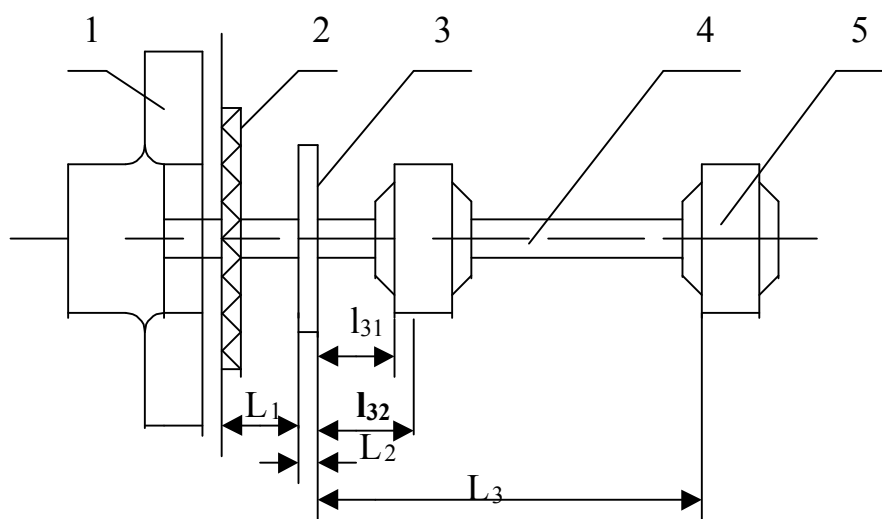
Расчётная схема опорного вала вентилятора для дымоудаления: 1 – рабочее колесо; 2 – тепловой экран; 3 – теплоотводящее устройство; 4 – промежуточный вал; 5 – опорный подшипник.
